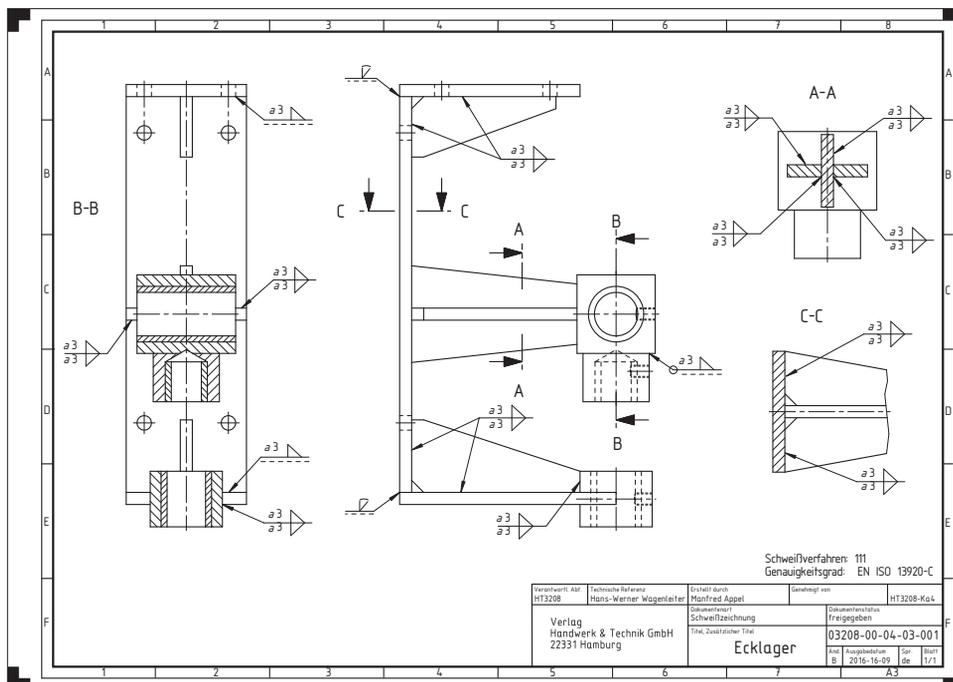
Schweißnahtbemaßung Ecklager
